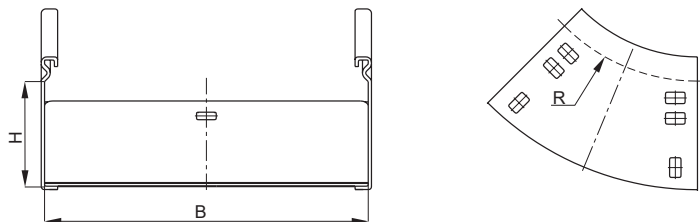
Поворот плавный 45° тип В10. Размеры для размещения кабеля / Figure C.2 – 45° smooth bend of B10 type. Dimensions for cable placement
